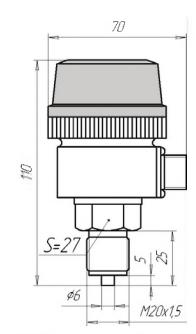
Модель 1020. Нержавеющий корпус, герморазъем.
